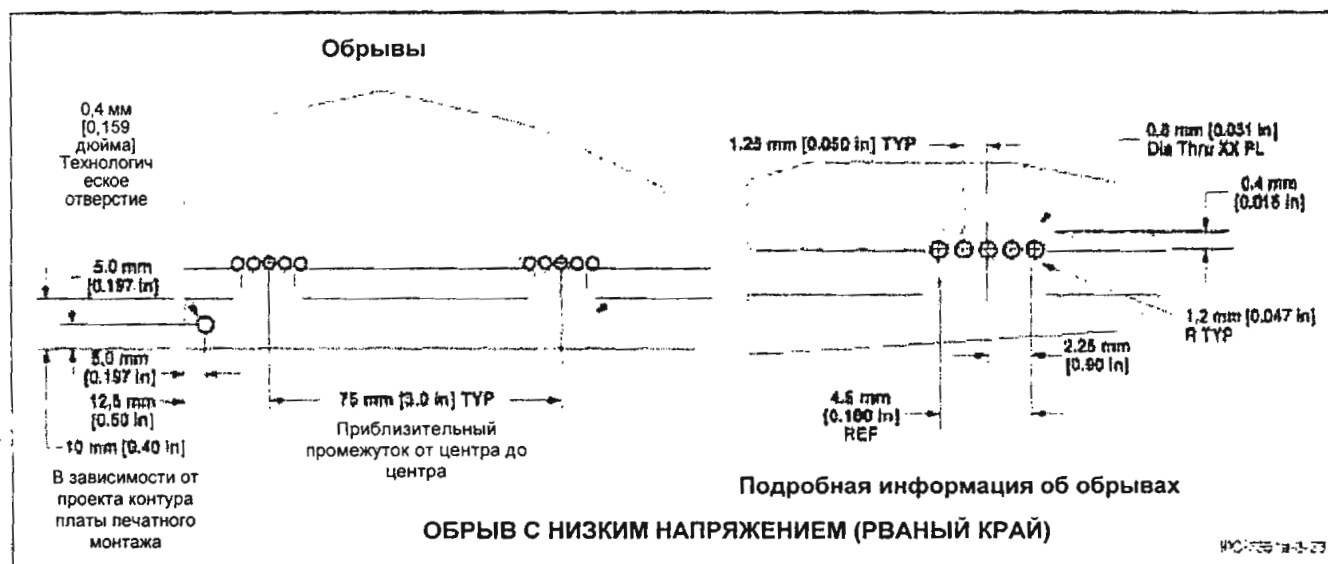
Обрыв (проложенный образец) с проложенными пазами
